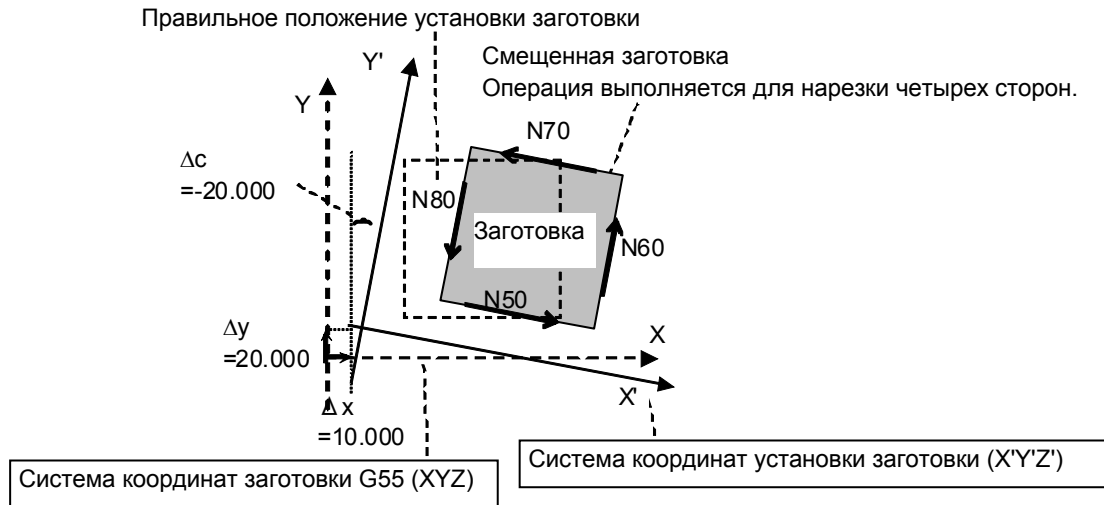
(y) Операция при наличии погрешности установки заготовки
